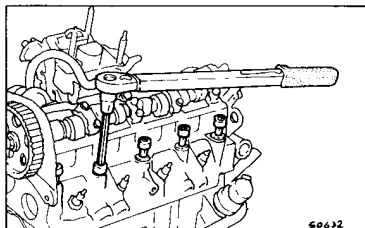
Снятие болтов крепления головки цилиндров
